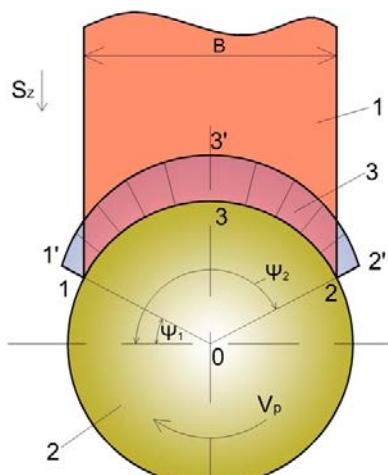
Схема фрезерования блока мяса цилиндрической фрезой
